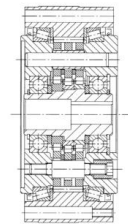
Конструкція модуля планетарно-цівкової передачі з 3 сателітами типу ЗК-V
